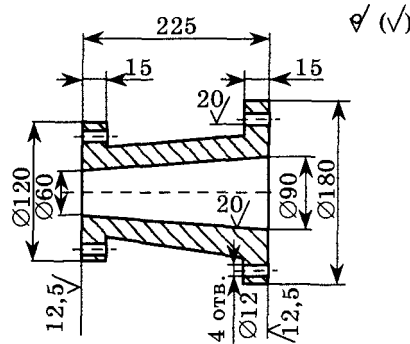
Чертеж детали: материал — СЧ20; класс точности размеров 9; ряд припусков 4
